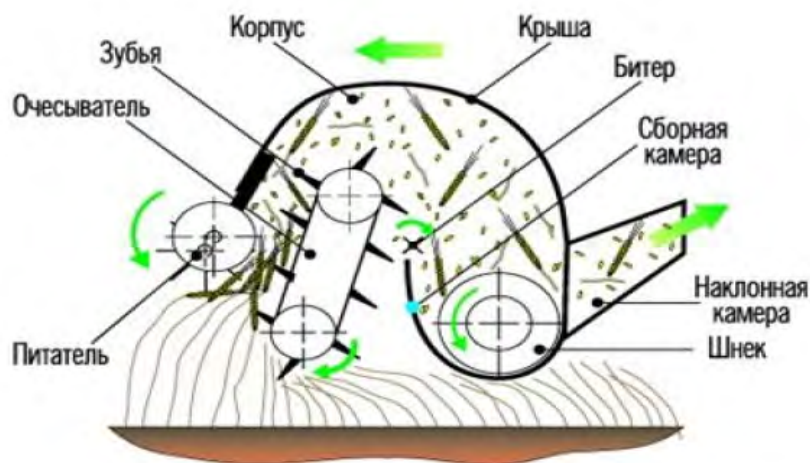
Конструктивная схема очесывающей жатки транспортерного типа
